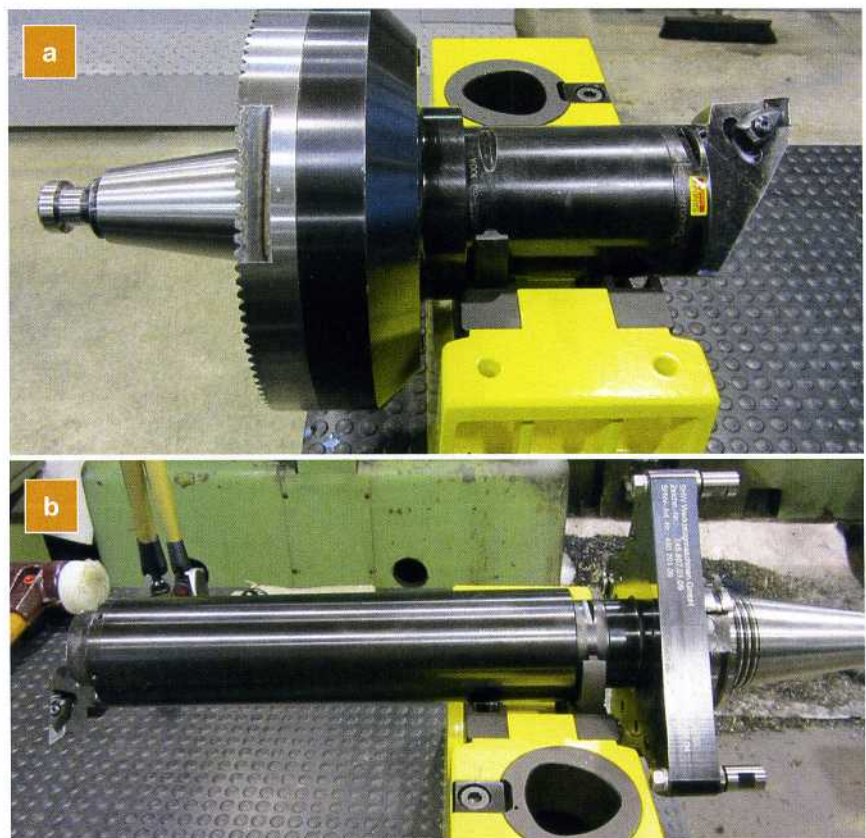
Die benötigten Werkzeuge für alle Dreh-, Fräs- und Bohroperationen liefert der Werkzeugwechsler mit Doppelgreifzange zuverlässig an den Fräskopf: a) Bei besonderen Anforderungen an die Stabilität kann ein Werkzeughalter mit Hirth-Verzahnung eingewechselt werden. b) Für einige Drehoperationen werden schwingungsgedämpfte „Silent Tools“ von Sandvik eingesetzt. Diese werden mit dem abgestützten Drehstahlhalter von SHW direkt aus dem Werkzeugwechsler eingewechselt.
